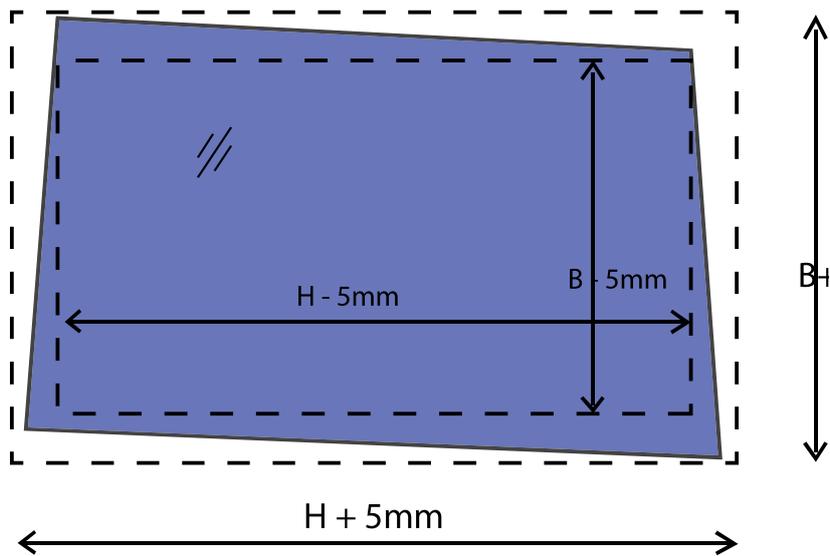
Rectangles de tolérances à largeur de fabrication et aux dimensions de fabrication et aux dimensions de fabrication.
